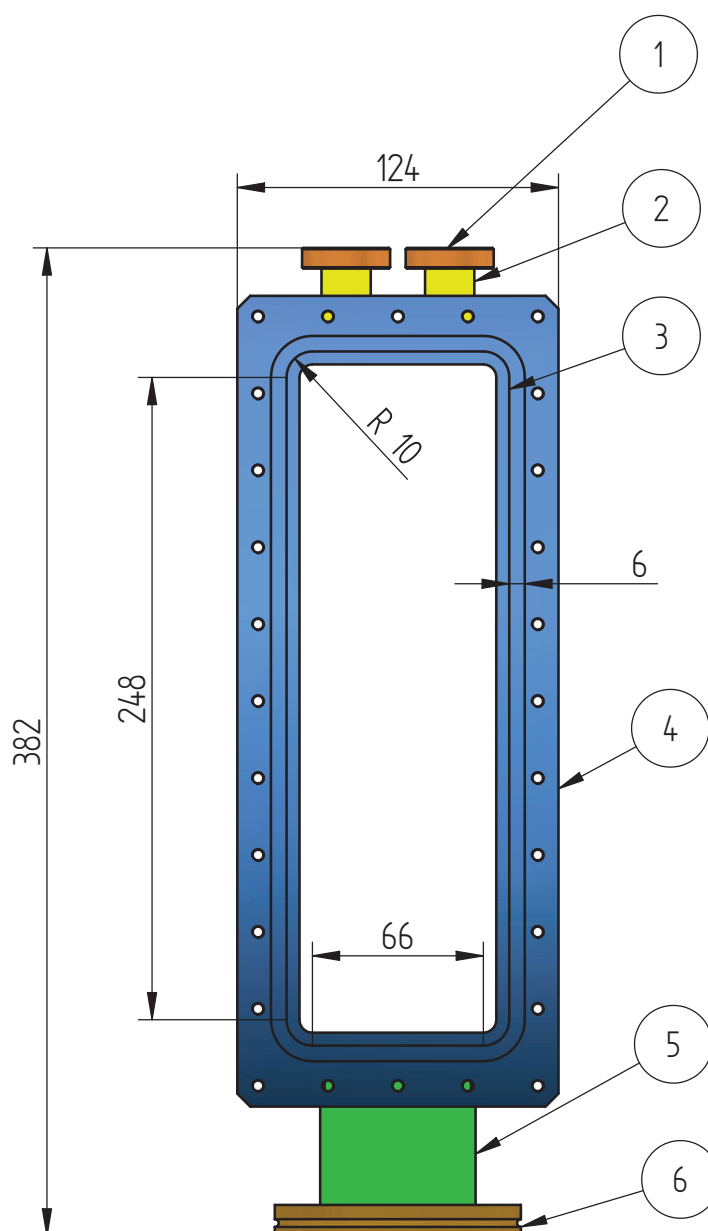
Bestandteile und wichtige Geometrie der Schweißgruppe
